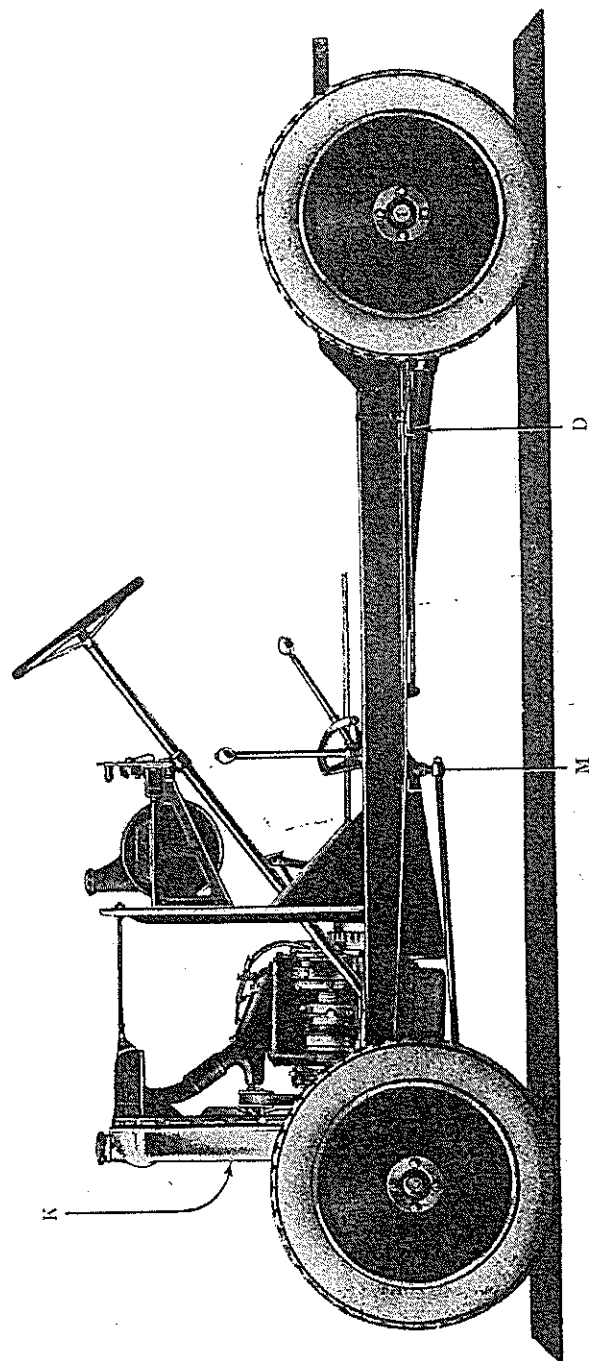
VUE EN ÉLEVATION DU CHASSIS 172 R.
